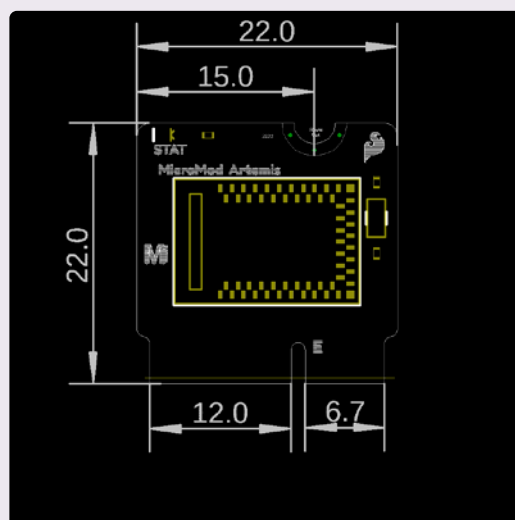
Chaque carte processeur est à la norme M.2 de „2222” ou 22 × 22 mm de taille hors tout.
